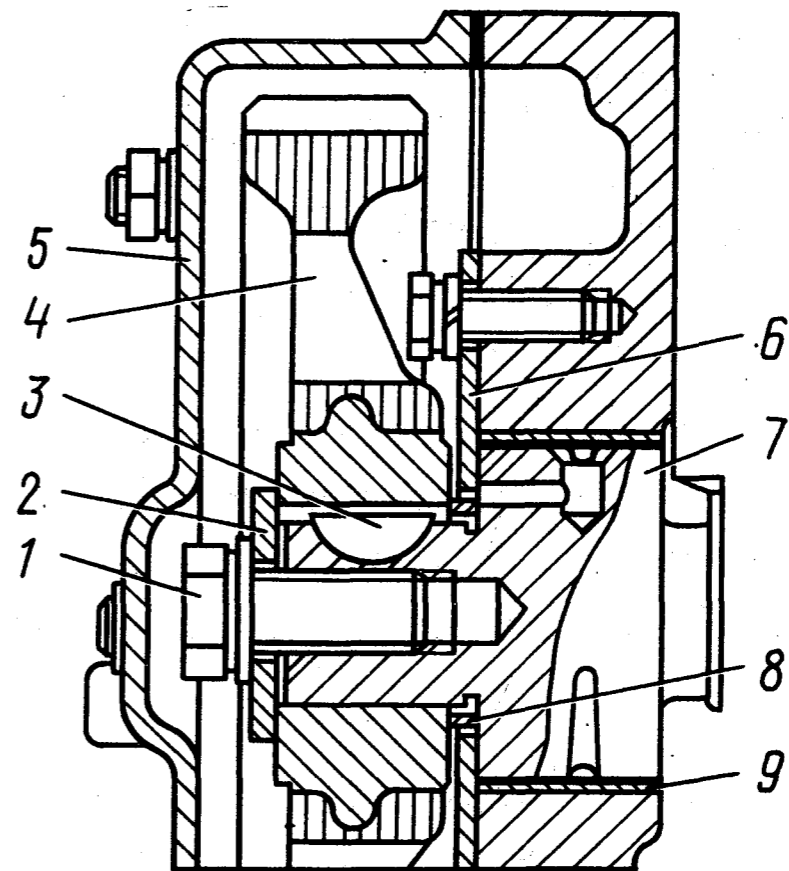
Привод распределительного вала: 1 - болт; 2 - шайба; 3 - шпилька; 4 - шестерня; 5 - крышка распределительных шестерен; 6 - фланец упорный; 7 - вал распределительный; 8 - втулка распорная; 9 - втулка распределительного вала
